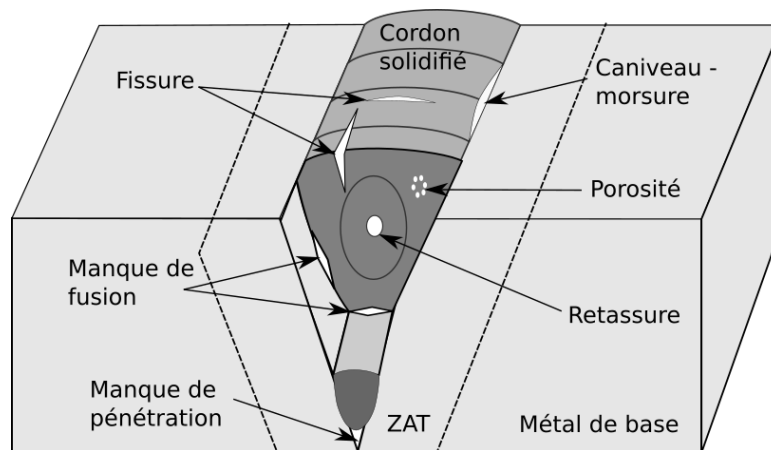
Représentation des défauts de soudage sur un assemblage.
